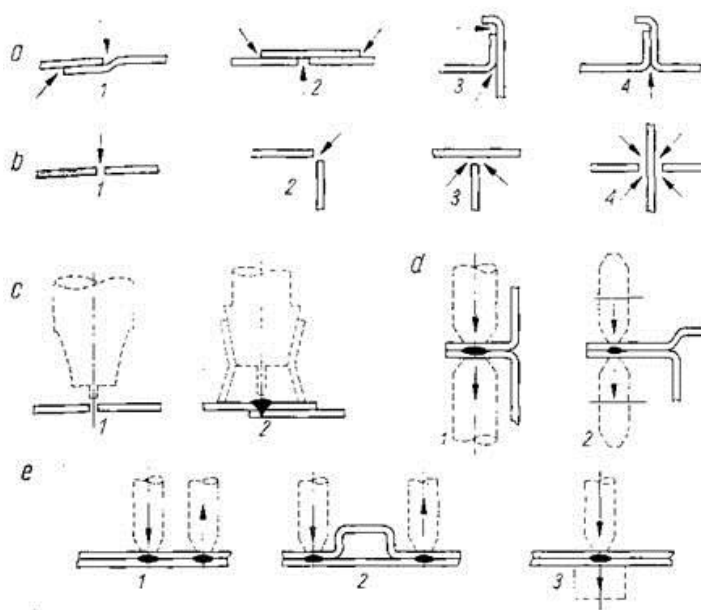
Неразъемные соединения кузовных деталей, выполняемые сваркой.
